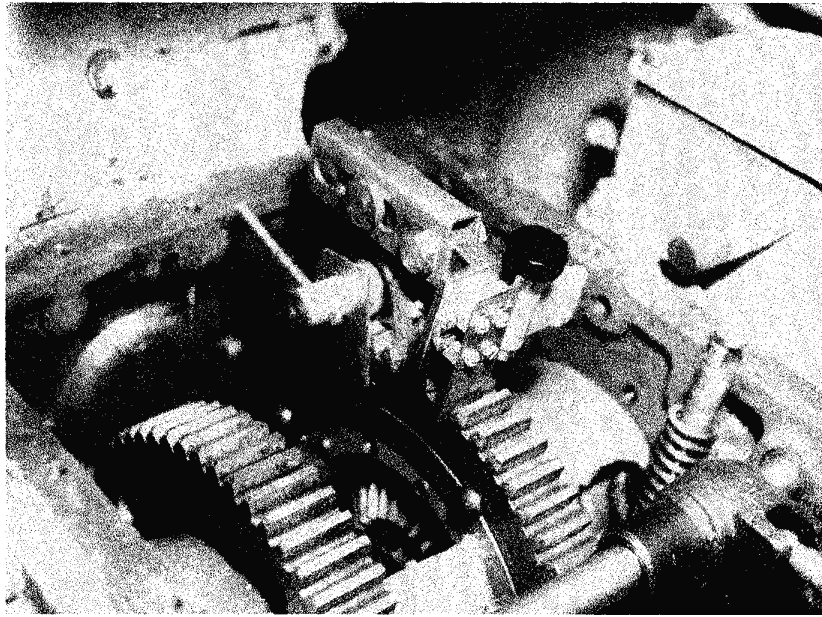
Загальний вигляд пристосування для нарізування канавок на зубах, встановленого на зубчастому колесі
